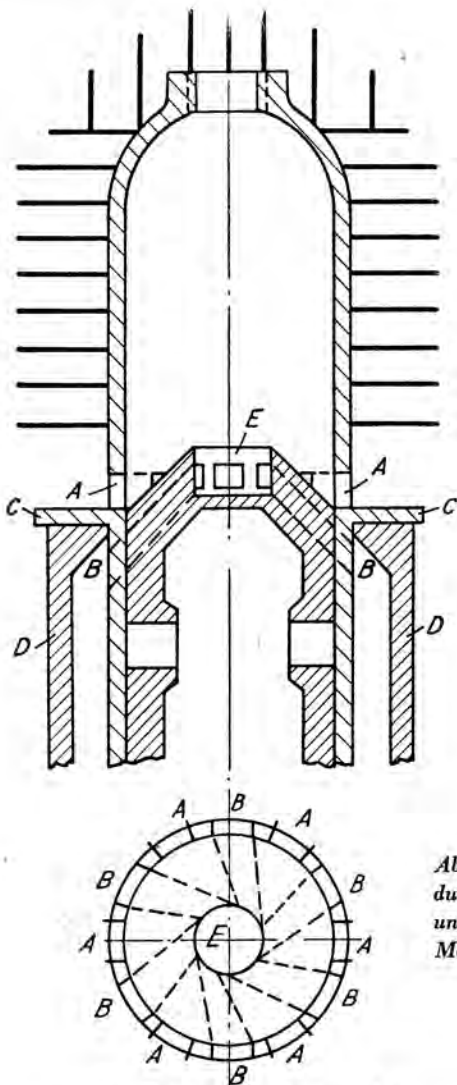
Schnitt durch Zylinder und Kolben des Motors von Rüdle
